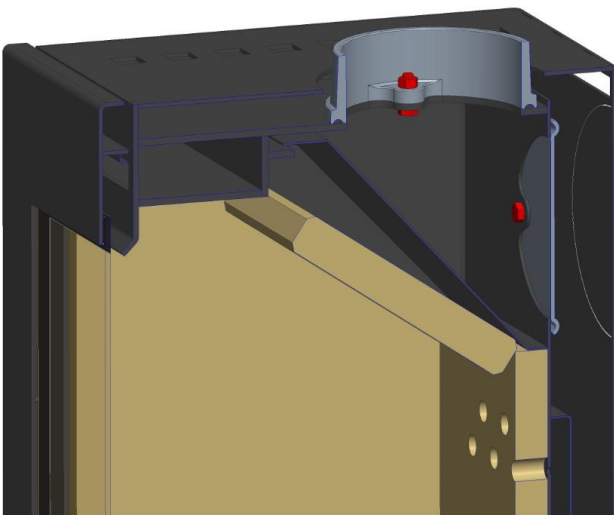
Ansicht Verschraubung Rauchrohrstutzen und horizontaler Blinddeckel
